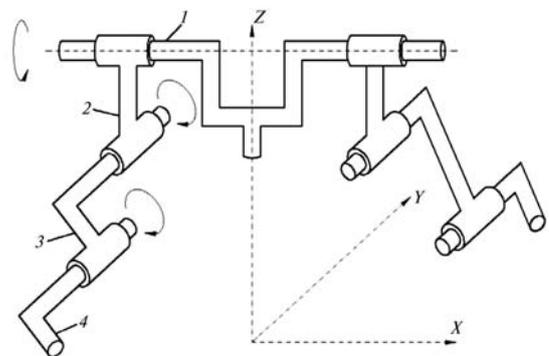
Кинематическая схема корпуса ДШР с руками:
